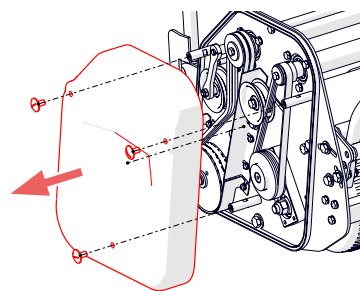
B – Die 3 äußeren Schrauben und die Abdeckung entfernen.
